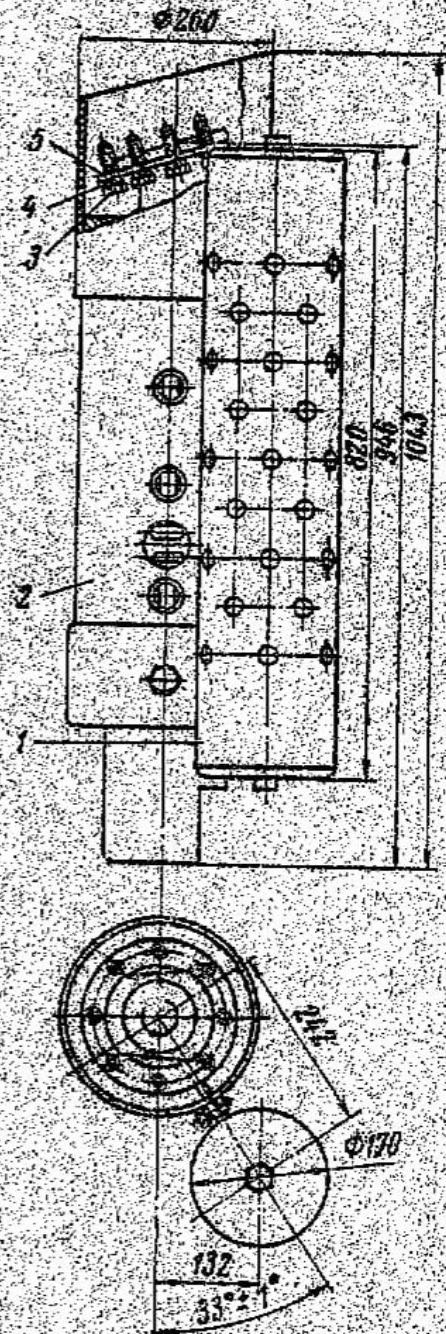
Общий вид дугогасительного устройства с шунтом.
